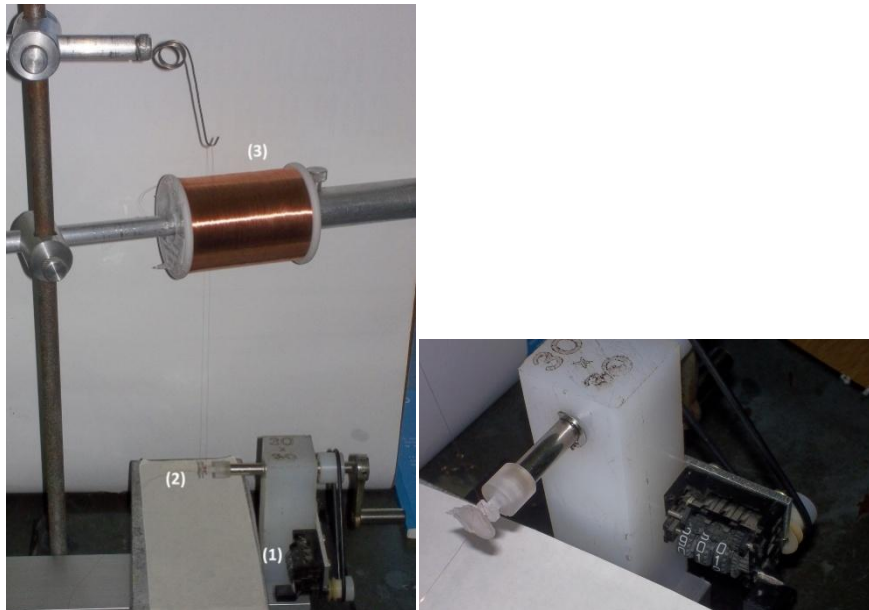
Bobinador: dispositivo utilizado para bobinar las bobinas, junto con una imagen de cómo debe ser colocada una bobina, (1) contador de vueltas, (2) bobina, (3) hilo de bobinar.
